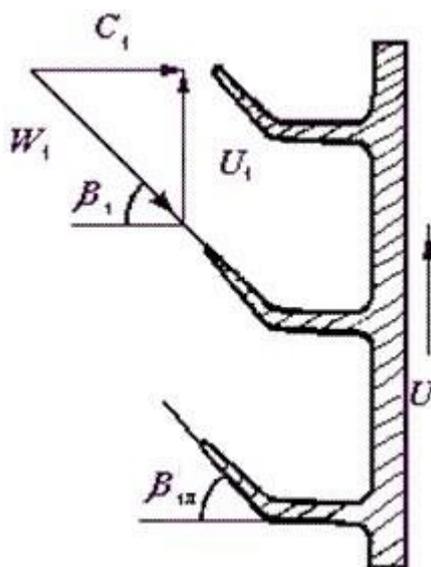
Плоскостное сечение рабочего колеса центробежного компрессора.
